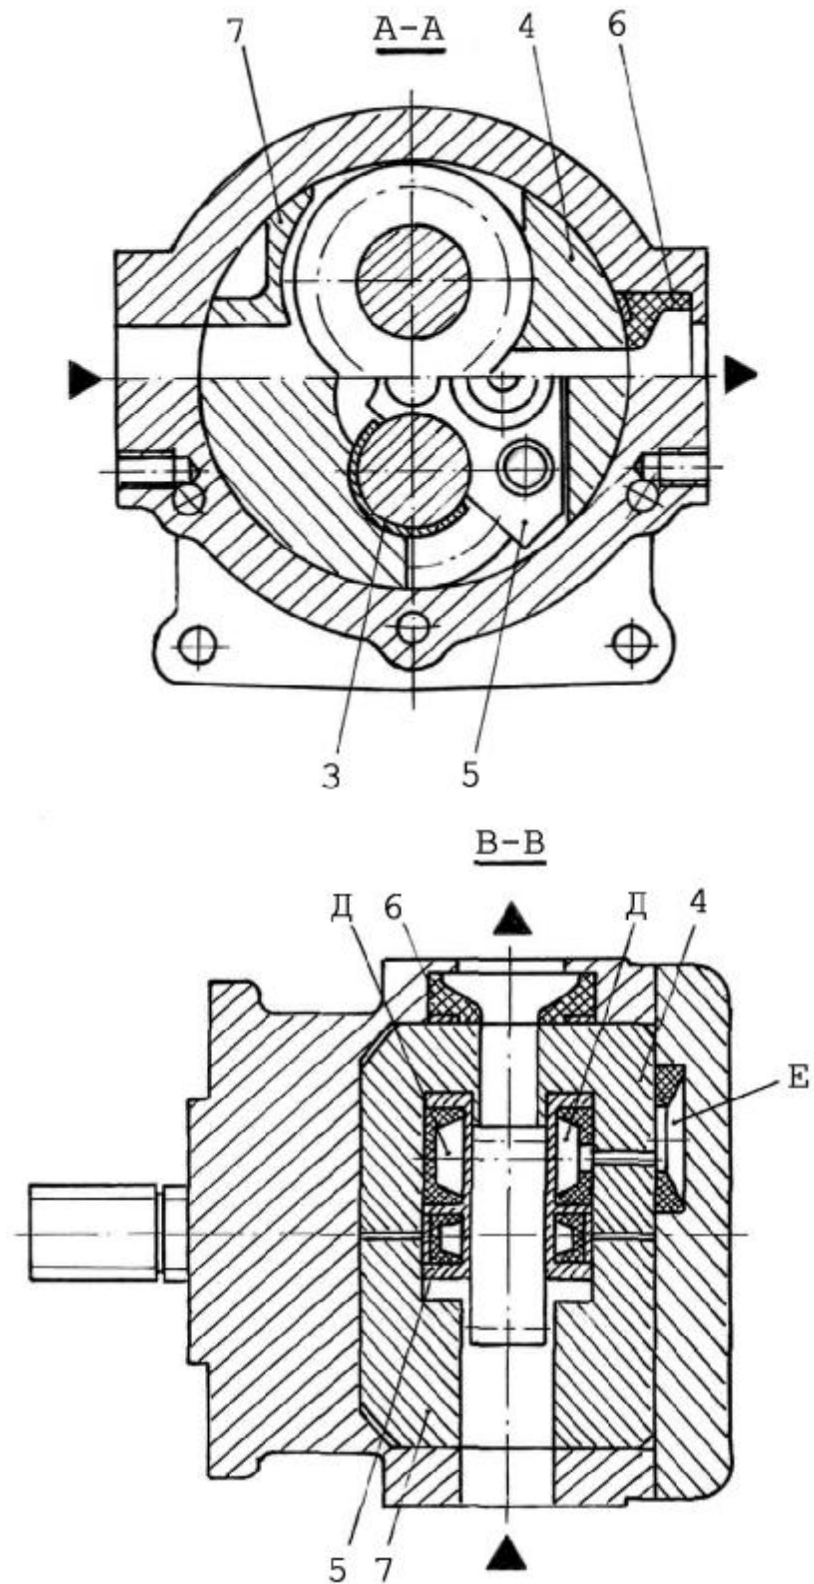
Насос шестеренный НШ – 32А: 1 – корпус; 2 и 8 – ведущий и ведомый валы; 3 – обойма подшипника скольжения; 4 –обойма поджимная; 5 – манжета торцового уплотнения; 6 – манжета радиального уплотнения; 7 - обойма подшипниковая; С, Д и Е – полости давления.
